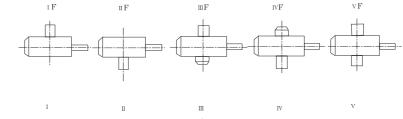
Drawing 3 WHX 系列减速器外形及安装尺寸
